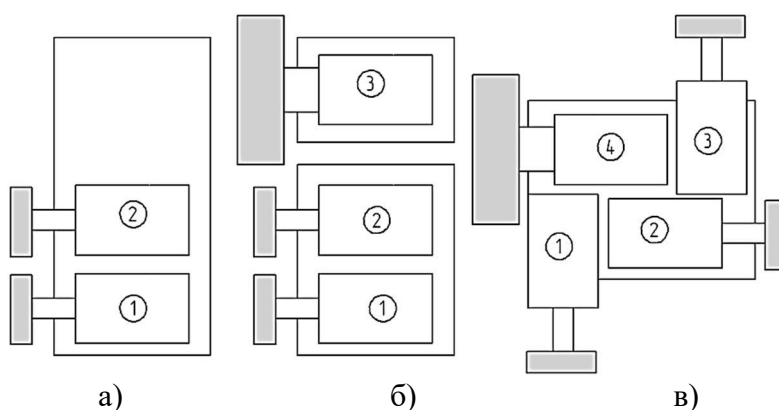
Примеры расположения шлифовальных шпинделей на современных станках с ЧПУ
